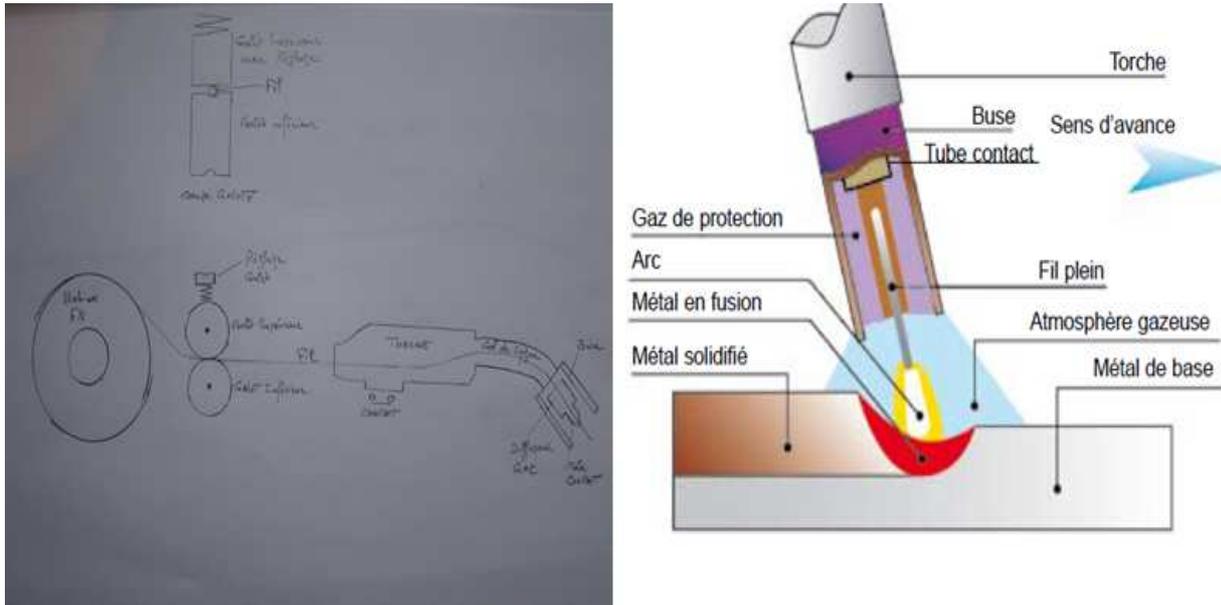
principe de fonctionnement du soudage MIG.
